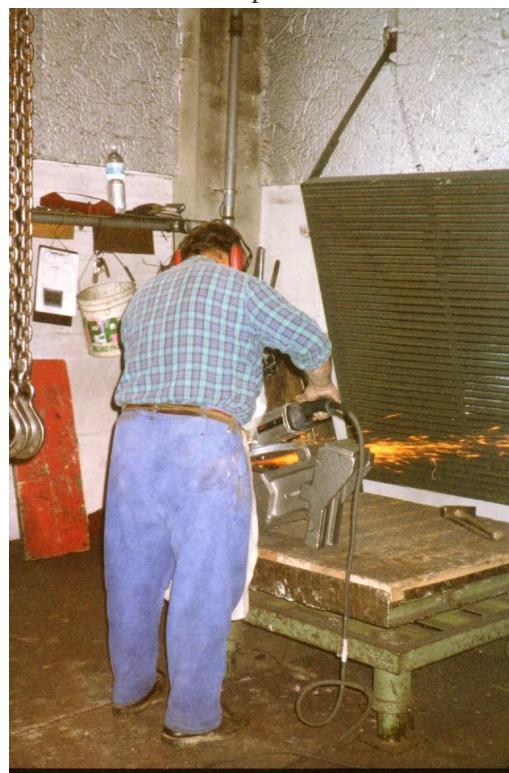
Addetto alla sbavatura dei getti con mola portatile
